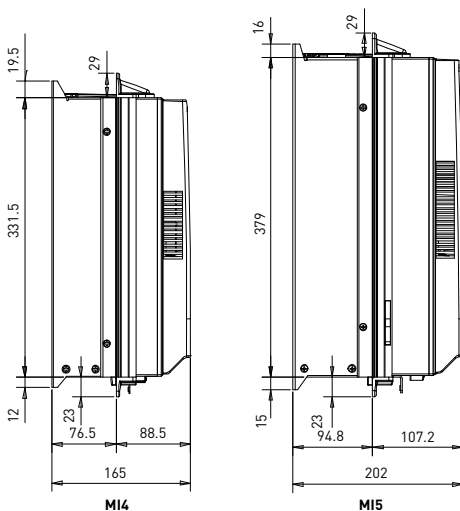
Размеры по глубине для фланцевого крепления приводов типоразмеров MI4 и MI5 (единица: мм)
